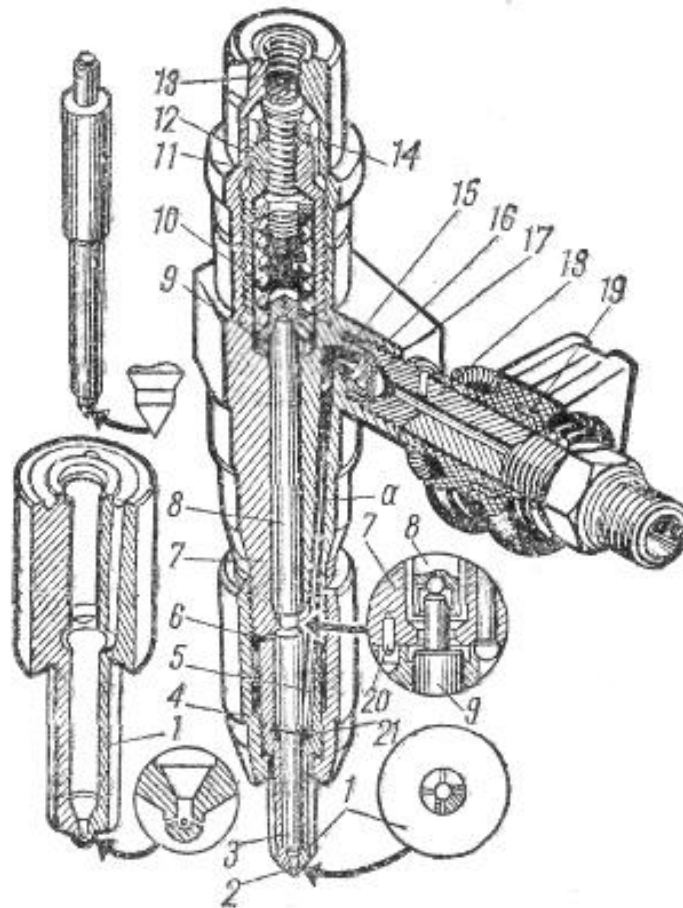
Форсунка ДВЗ ЯМЗ-236-238
